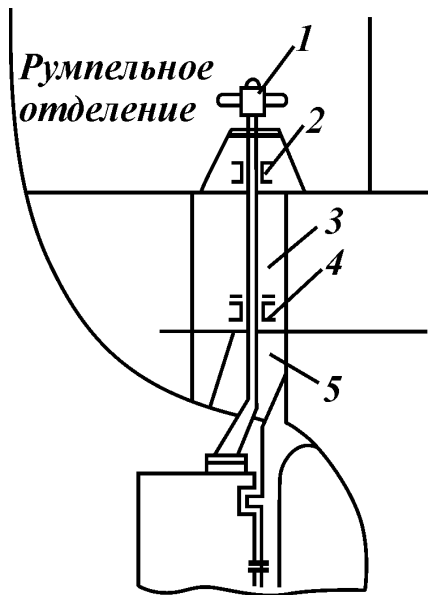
Расположение подшипников баллера (первый вариант): 1 – румпель рулевого привода; 2 – верхний опорный подшипник; 3 – баллер; 4 – нижний опорно-упорный подшипник; 5 – гелемпорт труба
